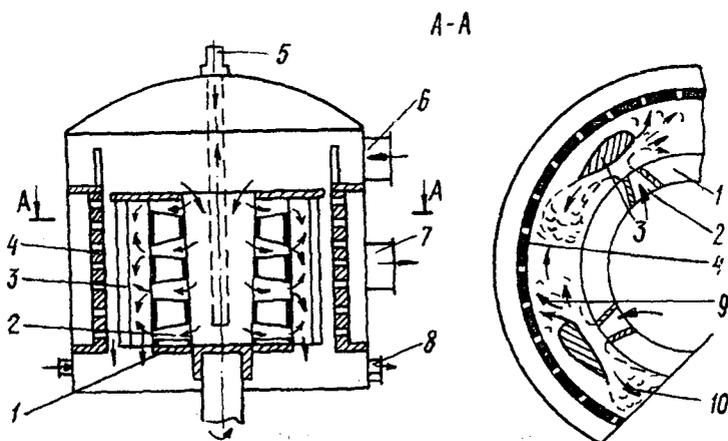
Конструкция узлоловителя с полым ротором: 1 – полый ротор; 2 – разгонные патрубки; 3 – лопасти; 4 – ситовый барабан; 5 – труба для разбавления массы в нижней части сортировки или удаления легких включений; 6 – входной патрубок; 7 – выходной патрубок; 8 – патрубок отходов сортирования; 9 – турбулентная струя перед лопастью; 10 – турбулентный хвост за лопастью
